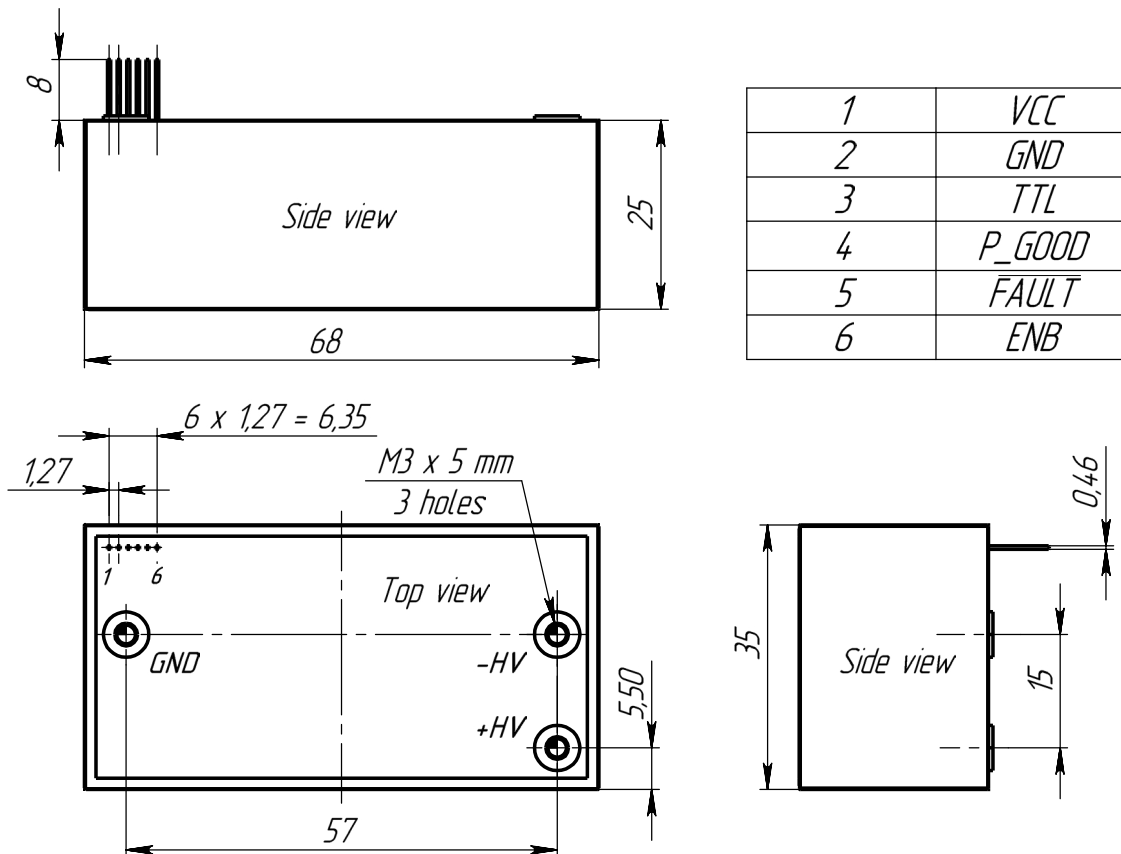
Чертеж и внешний вид коммутатора серии HVS-B1 в пластиковом корпусе для монтажа на печатную плату
